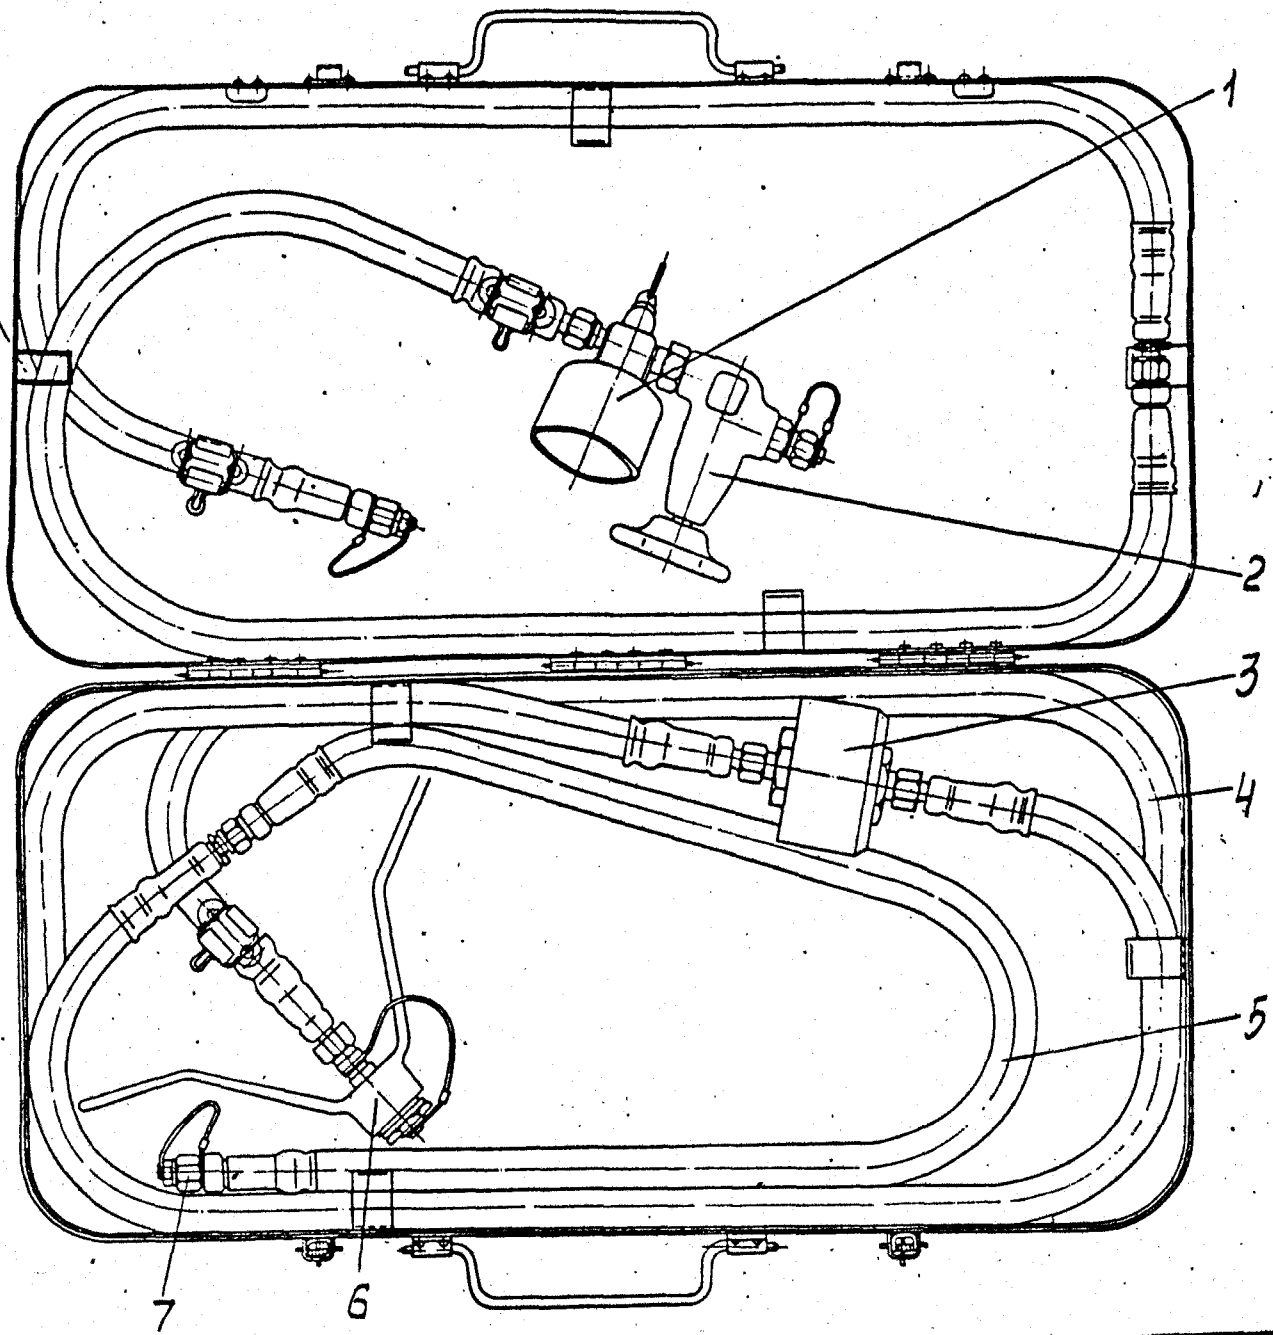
Приспособение для пневмозарядки и проверки давления агрегатов
